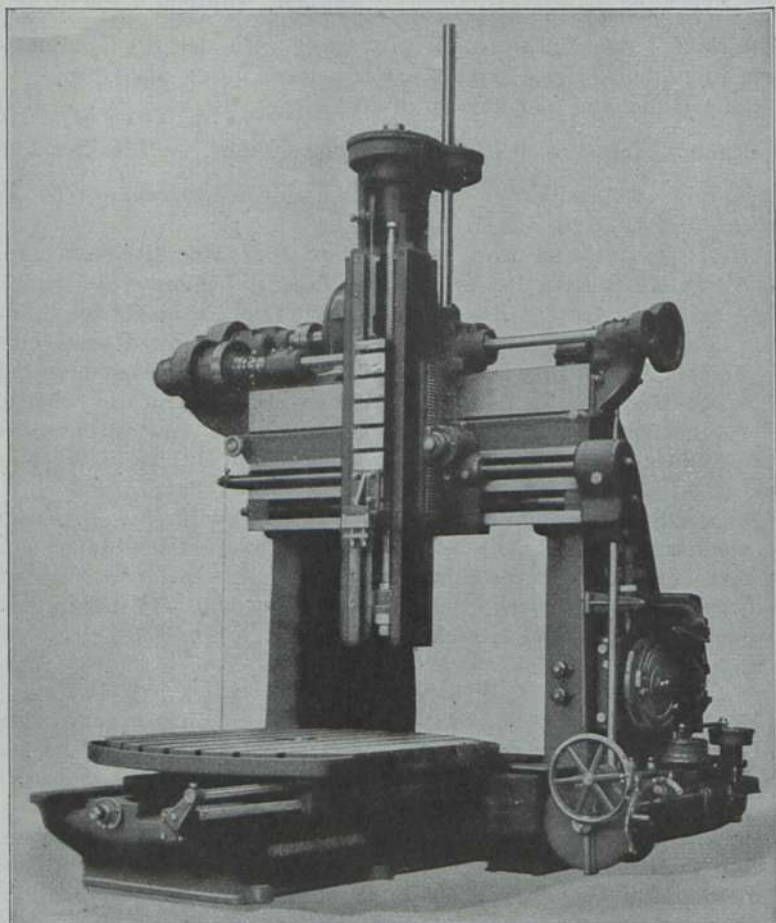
Schwere Stoßmaschine. Maschinenfabrik Schieß, A. G., Düsseldorf.
